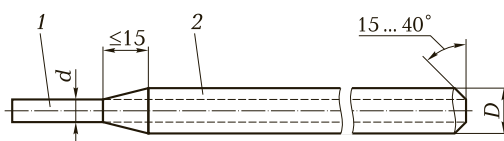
Схема покрытого электрода для ручной дуговой сварки:
